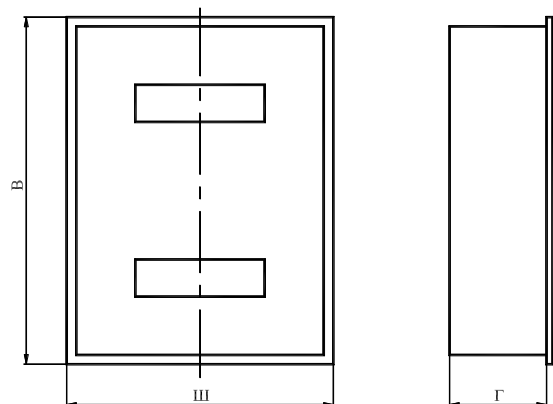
Габаритные размеры корпусов металлических ЩРВ
